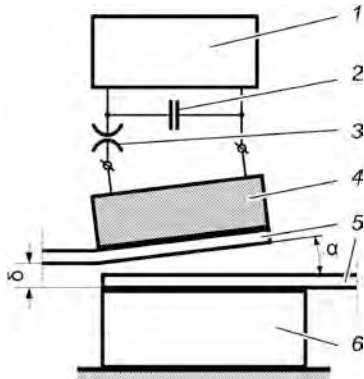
Схема установки для магнитно-импульсной сварки с косым соударением плоских свариваемых деталей: 1 — зарядное устройство; 2 — батарея конденсаторов высокого напряжения; 3 — блок управления, включающий разряд батареи высоковольтных конденсаторов; 4 — индуктор; 5 — свариваемые детали; 6 — массивная опора
